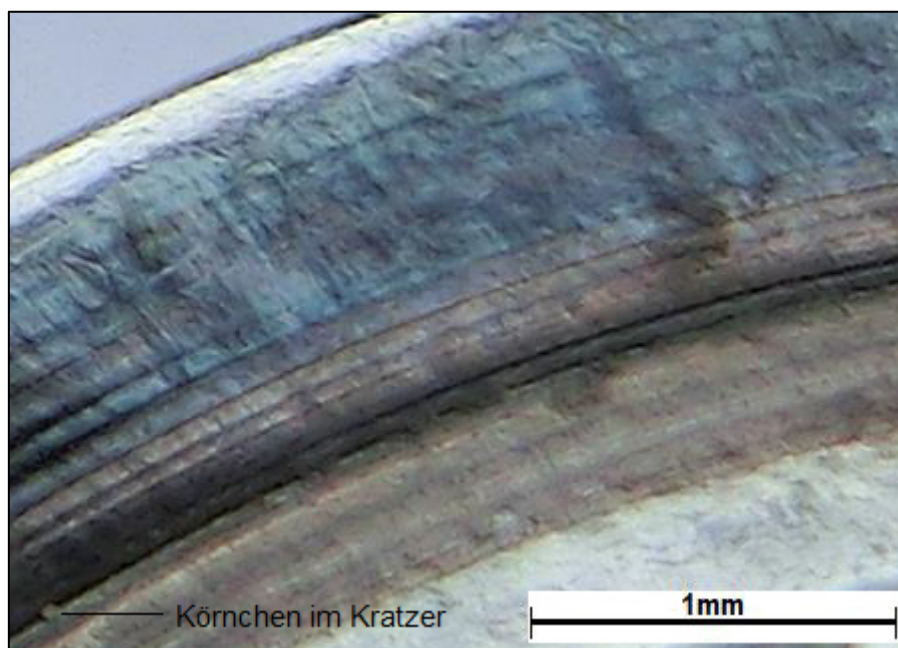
Kratzer auf der Gewindeflanke einer Stahl-Spindel
